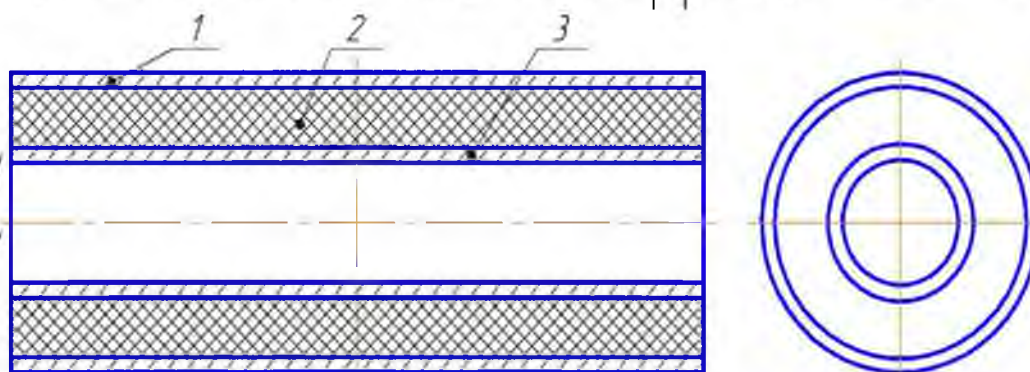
Конструкція втулки блока: 1 – зовнішня втулка; 2 – пружнодемпфуючий елемент; 3 – внутрішня втулка
